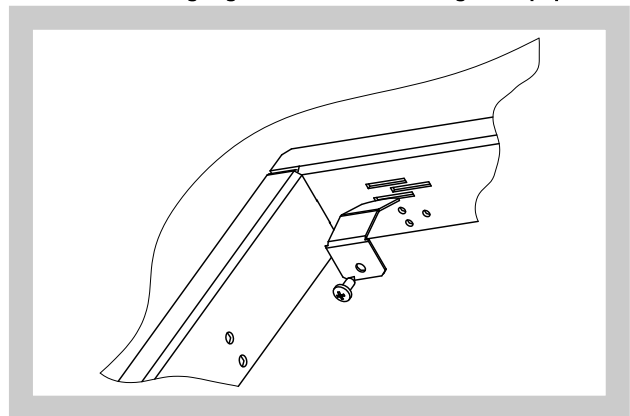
Befestigungsrahmen mit Halterung für Gipsplatte
